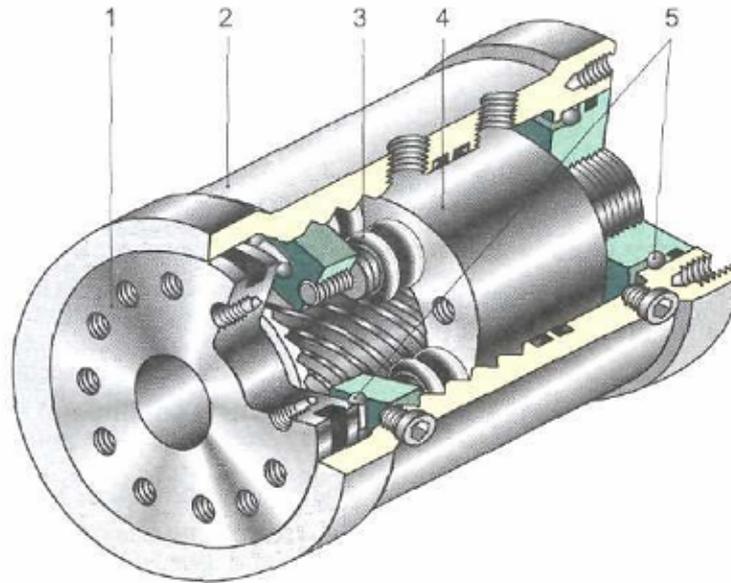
Поршневой гидродвигатель с винтовым преобразованием. 1 –вал; 2 – корпус; 3 –группа роликов; 4 –поршень; 5 –радиально – упорные подшипники.
